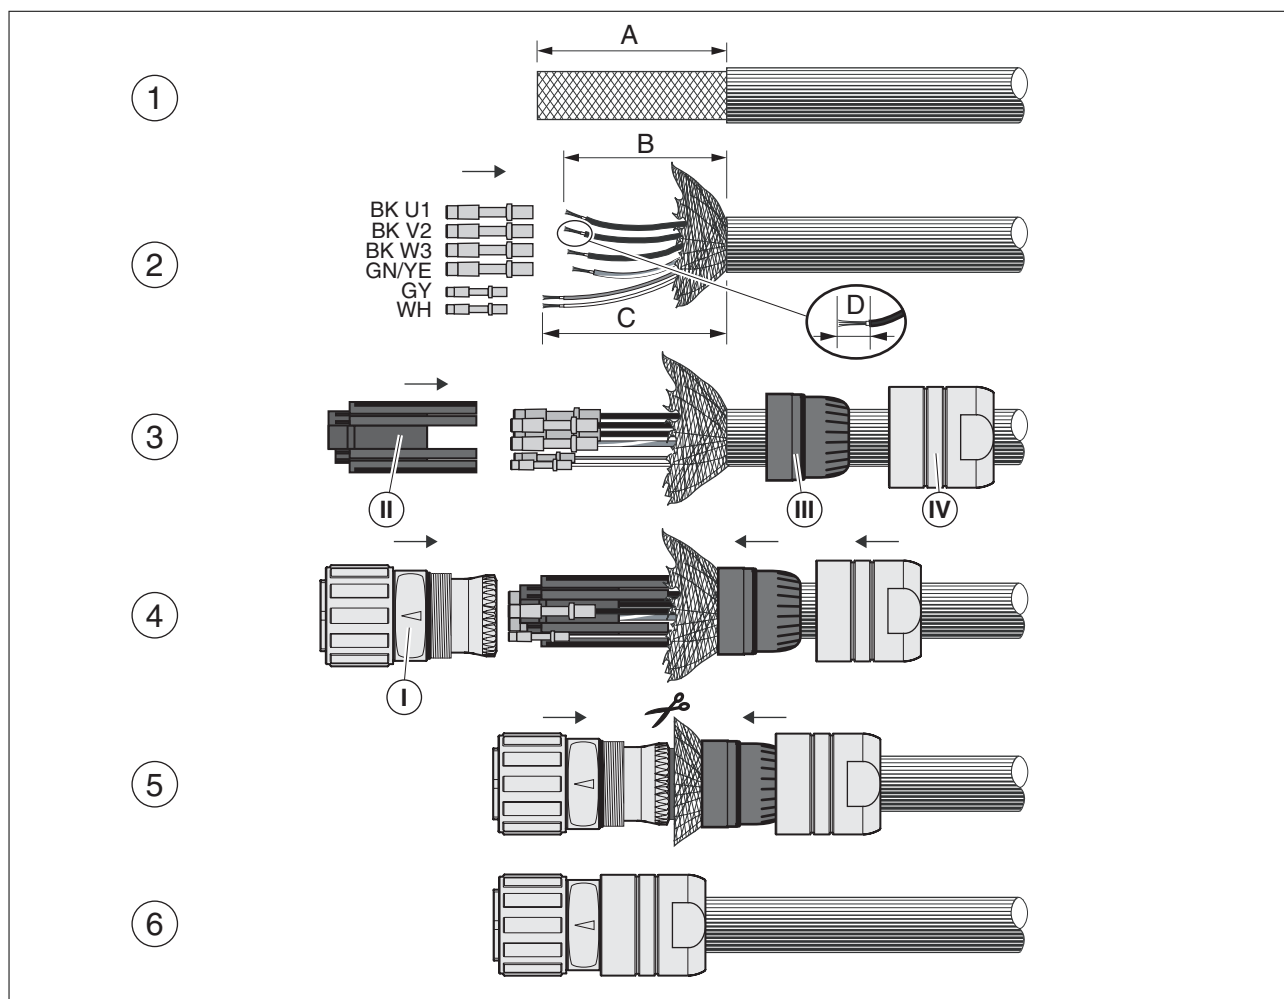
Assemblare il cavo motore con connettore motore M40
